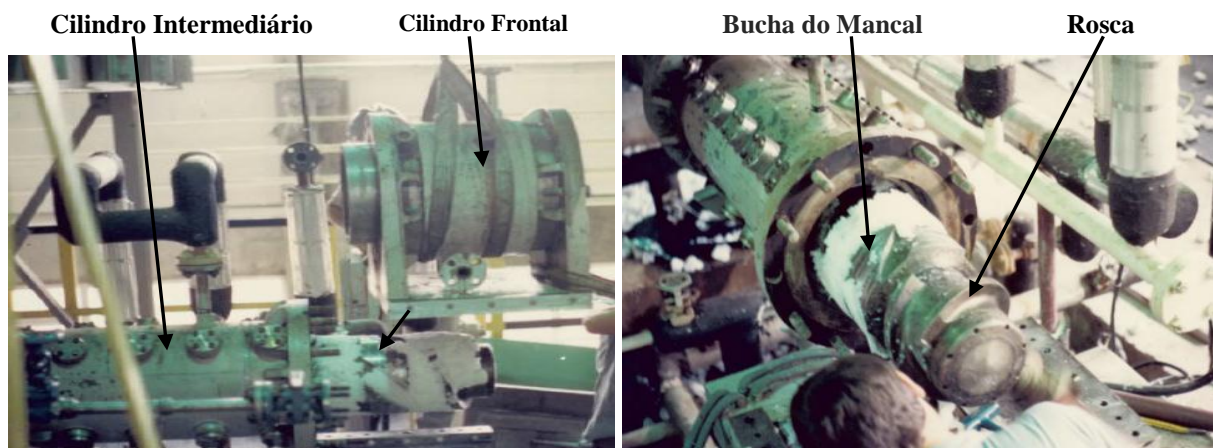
Desmontagem da parte frontal da extrusora monorosca para acesso ao conjunto mancal para inspeção.
